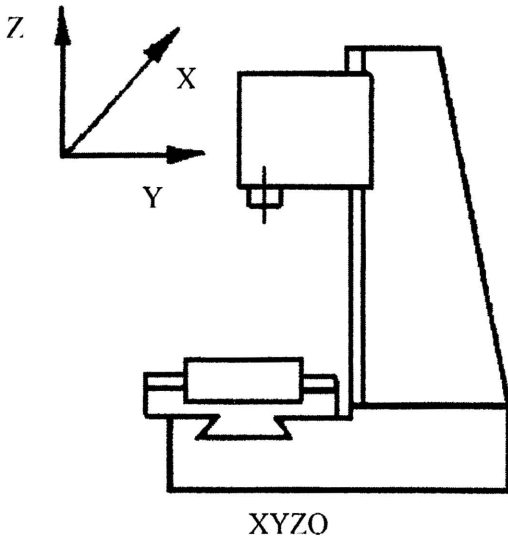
Компонка бесконсольно-фрезерных станков
